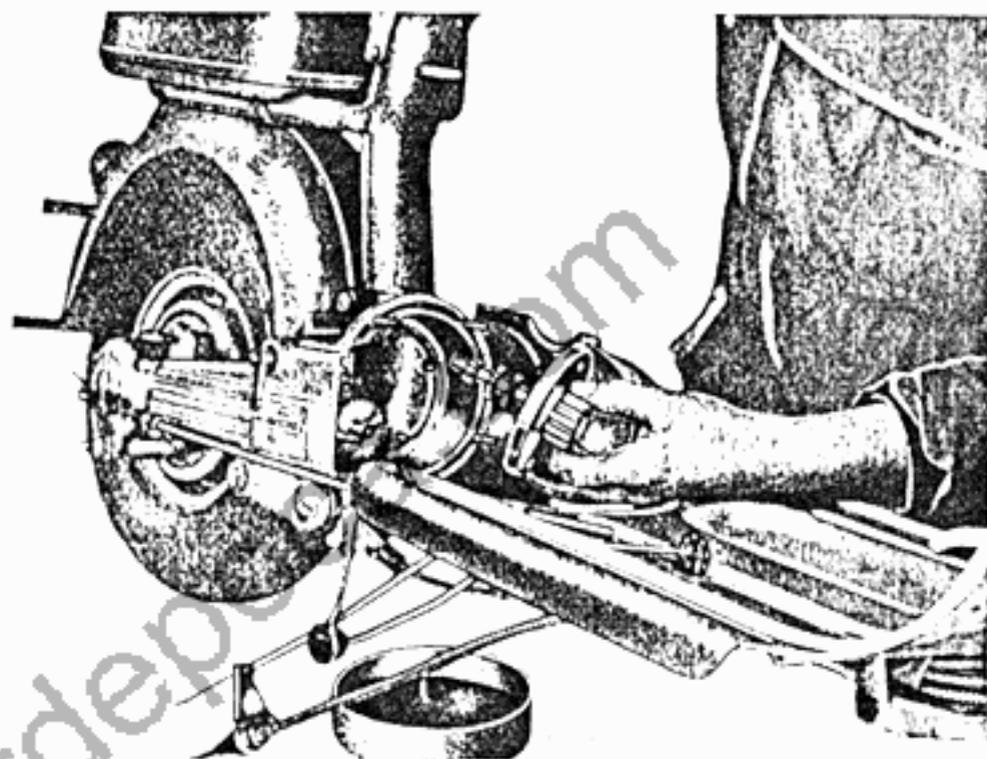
Rimontaggio albero primario e flangia di supporto
